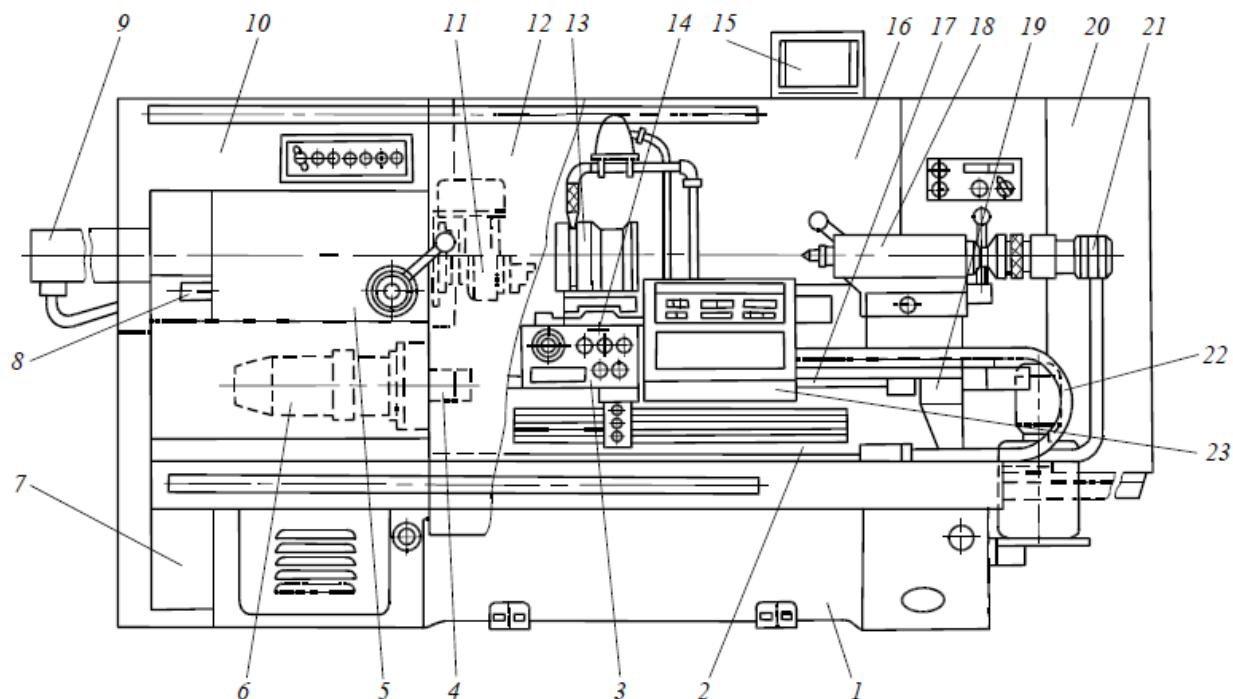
Общий вид станка мод. 16K20Ф3
